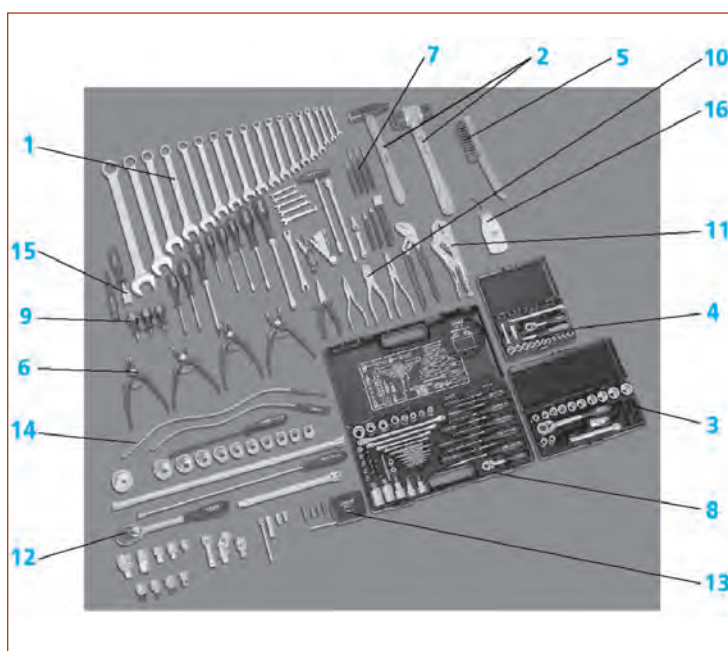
Grundausrüstung wichtiger Handwerkzeuge.
